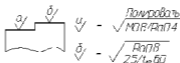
Упрощенное обозначение шероховатости поверхностей
